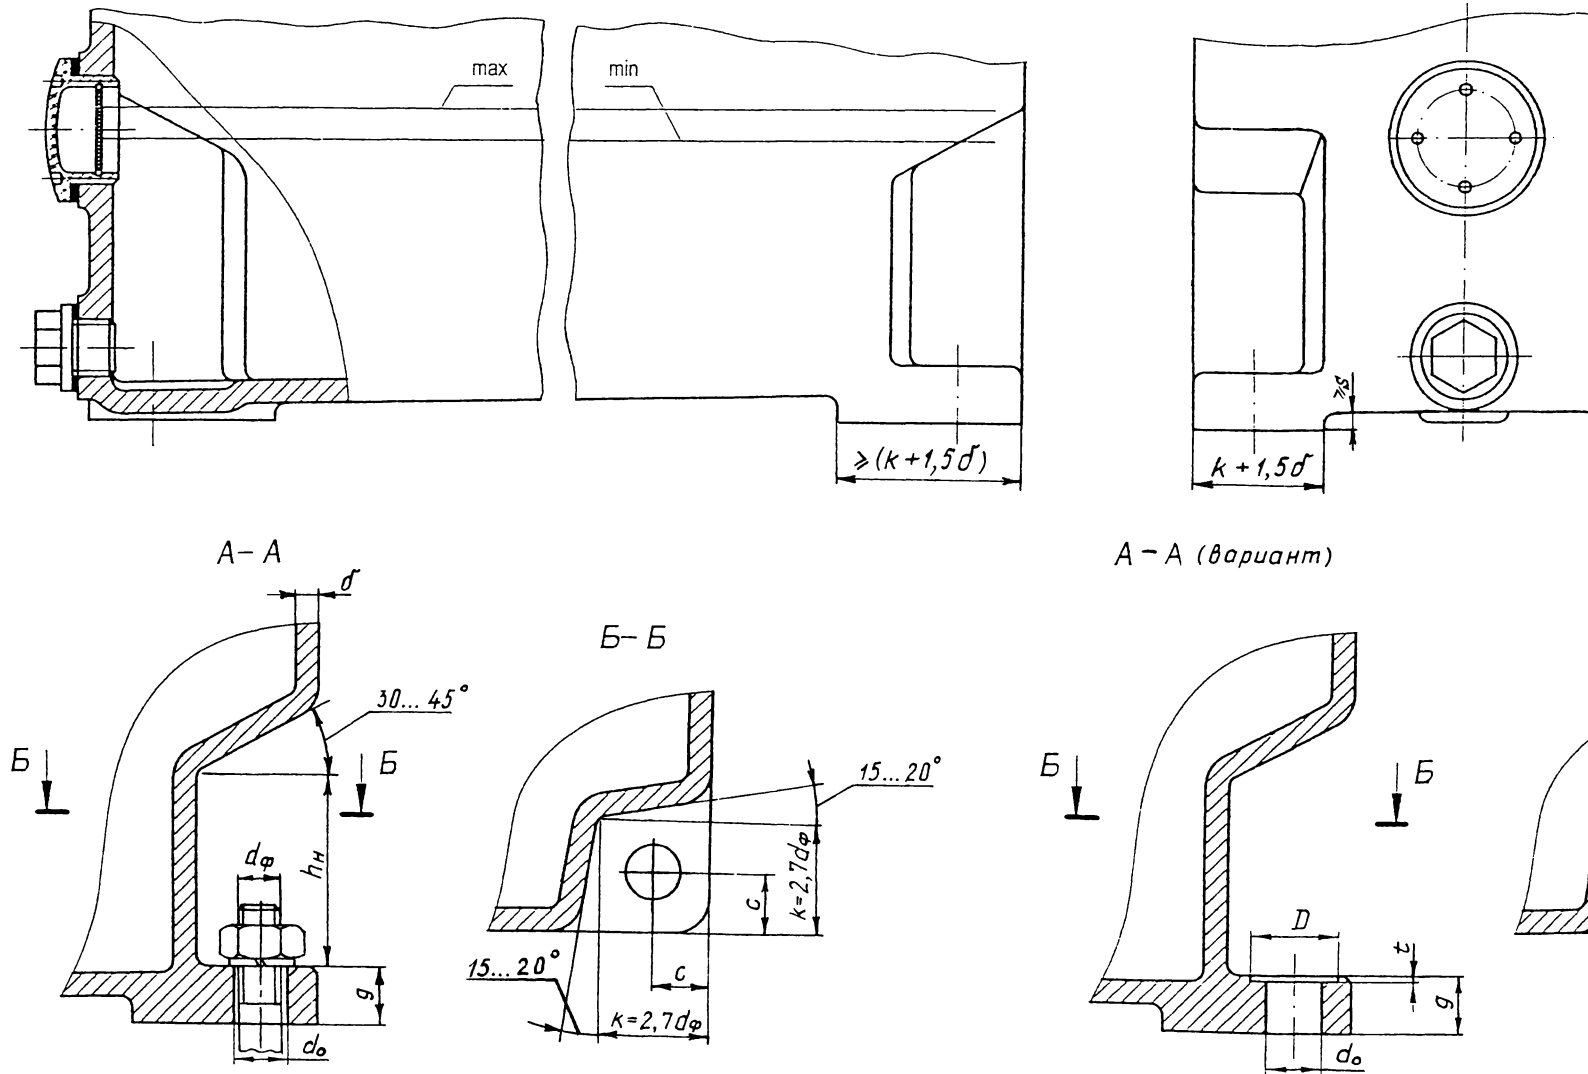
Лапы для крепления корпуса к плите (раме) (размеры см. в табл. 11.2.1)
